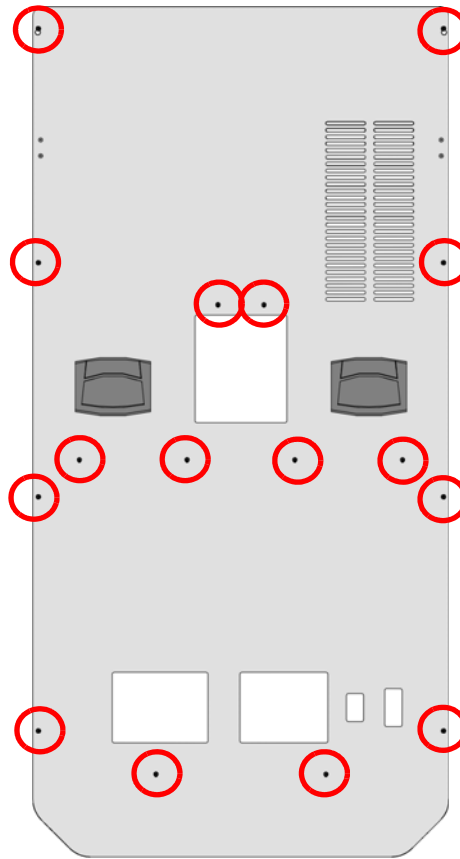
Positionen der Befestigungsschrauben für das hintere Panel
